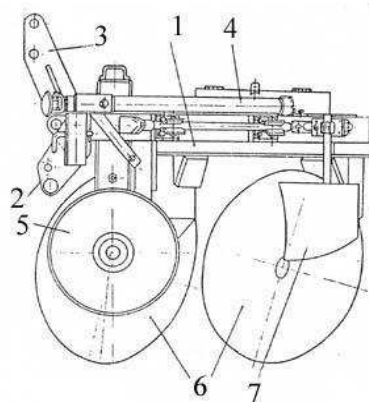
Плуг дисковый противопожарный ПДП-1,2: 1 – рама; 2 – проушина; 3 – стойка; 4 – аутригер; 5 – опорное колесо; 6 – сферический диск; 7 – чистик
